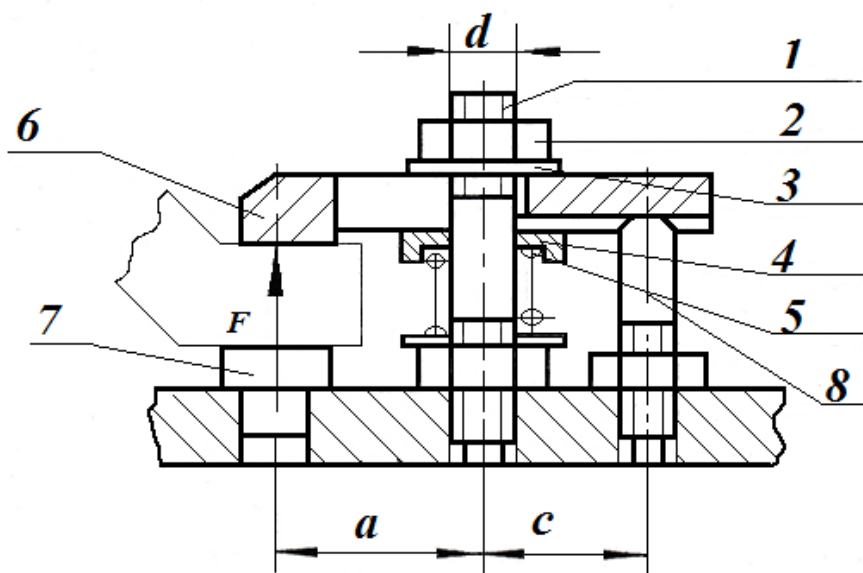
Станочный прихват: 1 – шпилька; 2 – гайка; 3, 4 – шайбы; 5 – пружина; 6 – планка; 7 – упор; 8 – стойка
